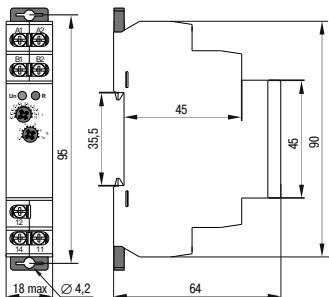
Габаритные и установочные размеры реле / Figure 1 - Overall and mounting dimensions of the relay
